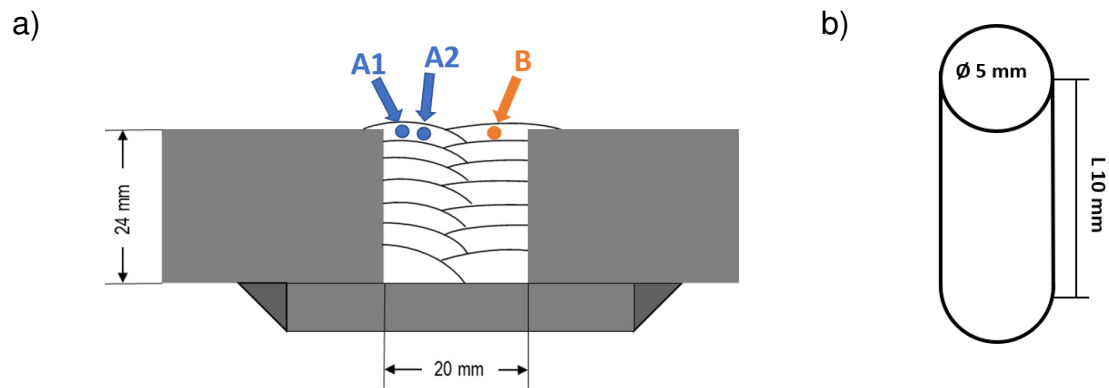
a) Skizze des Schweißquerschnitts zur Veranschaulichung der Probenentnahme und in b) Skizze einer Dilatometerprobe.
